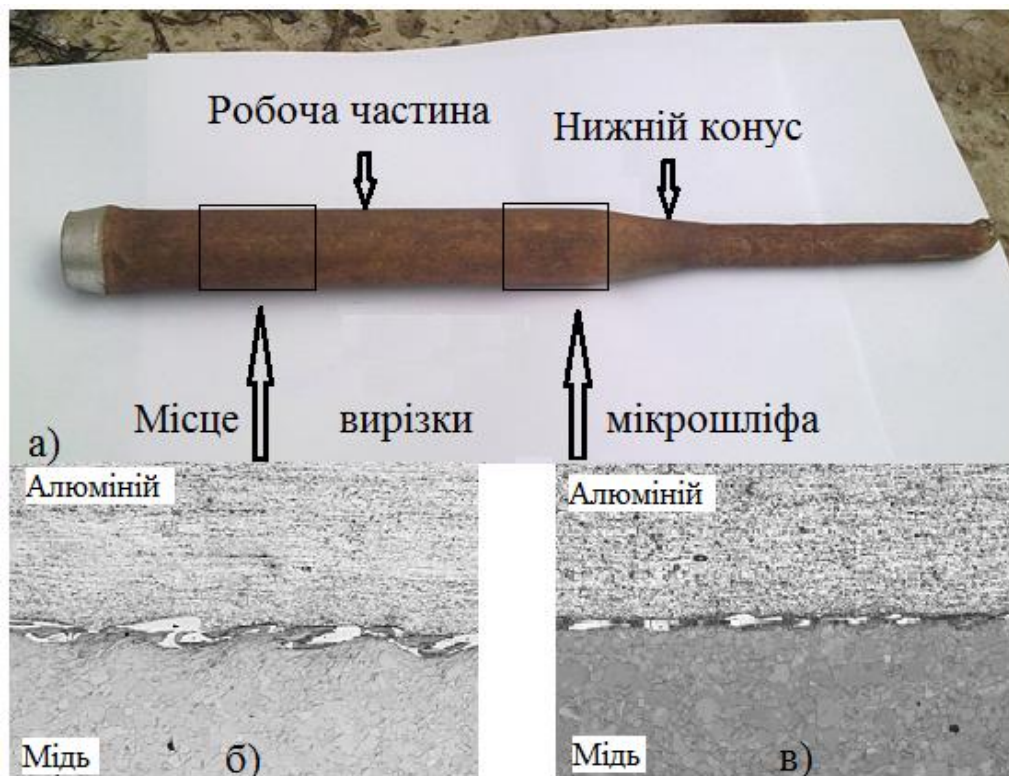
Заготовка після ЗВ (а) і мікроструктура зони з'єднання в різних частинах заготовки (б, в) (x100)
